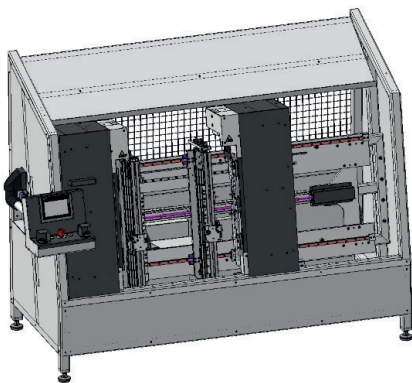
Schubkasten-Montagevorrichtung AvanFit 400
